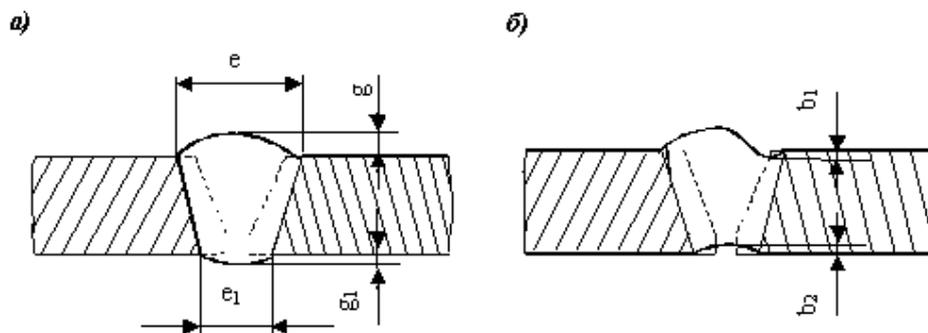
Размеры сварного шва, подлежащие измерениям при ВИК
